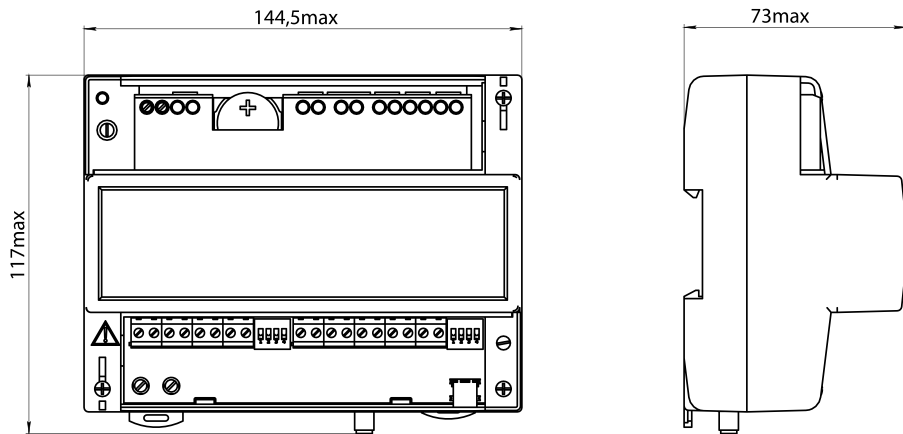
Общий вид и габаритные размеры УСПД со снятыми крышками зажимов
